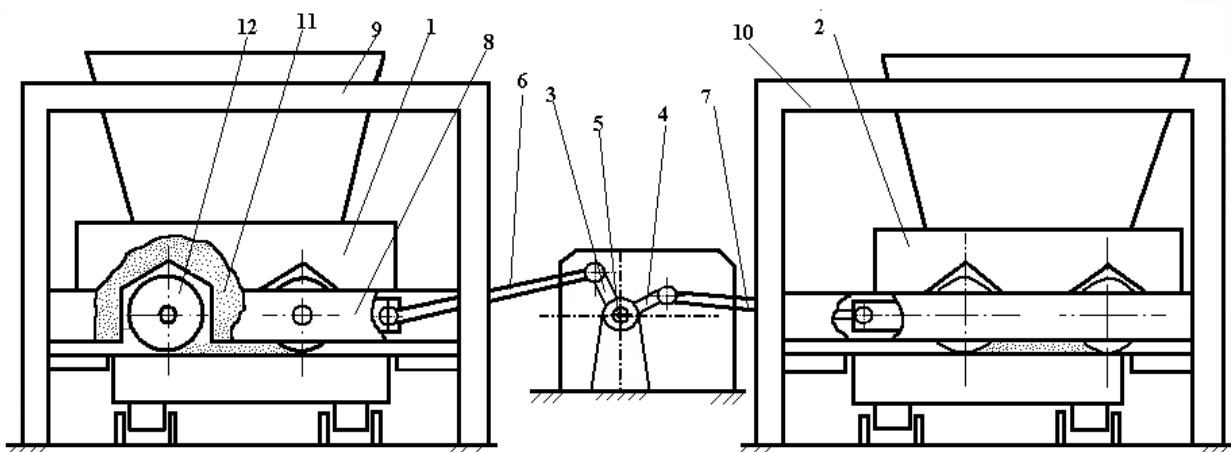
Роликова формувальна установка з рекупераційним приводом
